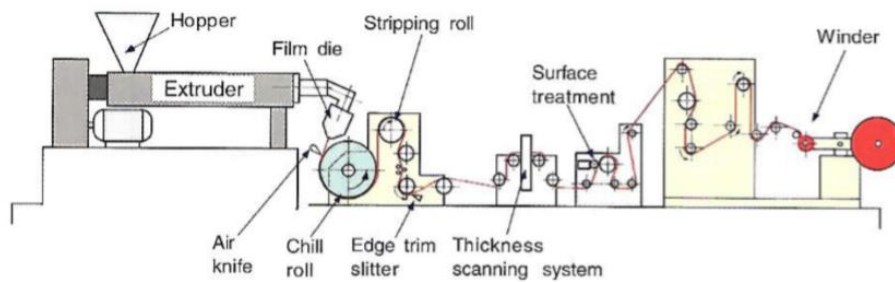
37 Componentes de una línea de extrusión de películas moldeadas
